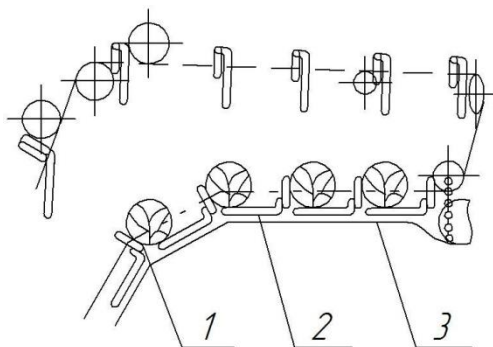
Схема скребкового елеватора з нижньою гілкою транспортування: 1 – транспортувальна пластина, 2 – скребок, 3 – сталевий настил.
